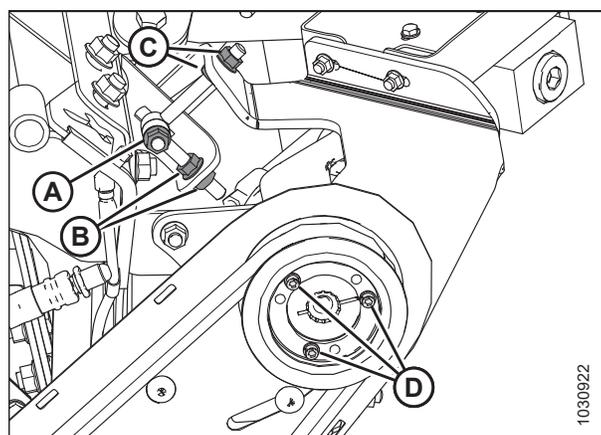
Ведущий шкив — Гидромотор привода плющилки
